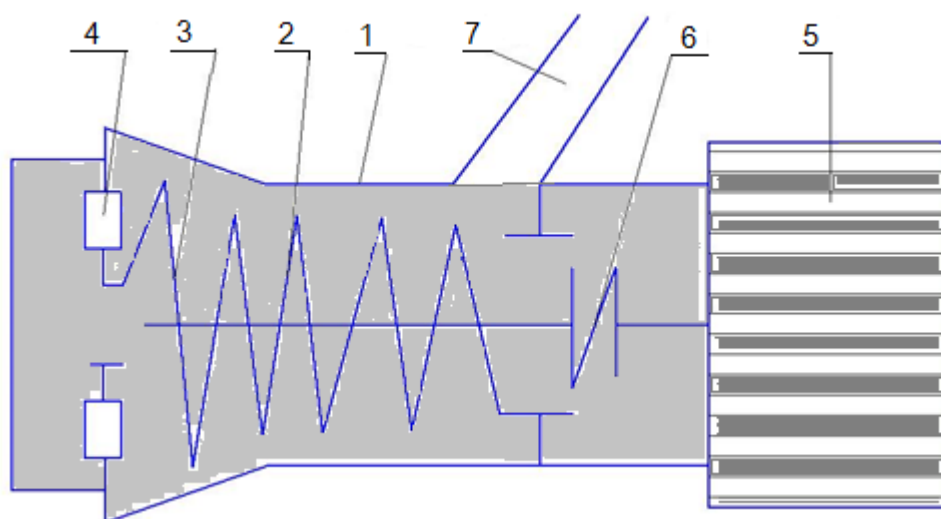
Пристрій для транспортування гною: 1 – циліндричний корпус; 2 – гвинт основний; 3 – гвинт допоміжний; 4 – завантажувальні отвори; 5 – електропривід; 6 – муфта; 7 – напірний патрубок.
